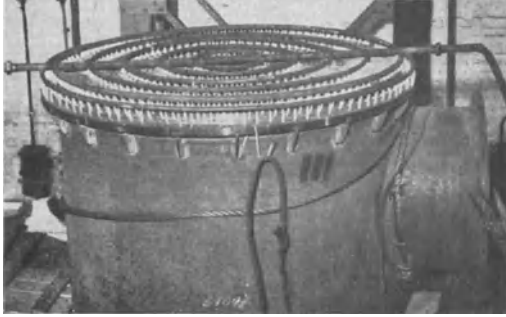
Leuchtgasheizvorrichtung für Schweißnähte.
